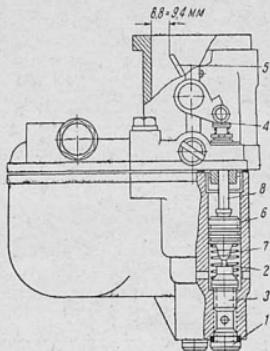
Регулировка клапана экономайзера карбюратора МКЗ-6
